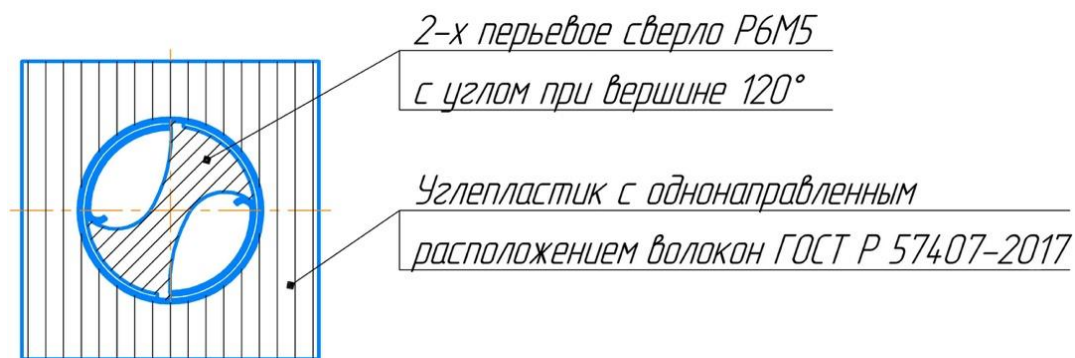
Схема контакта заготовки и инструмента в процессе сверления
